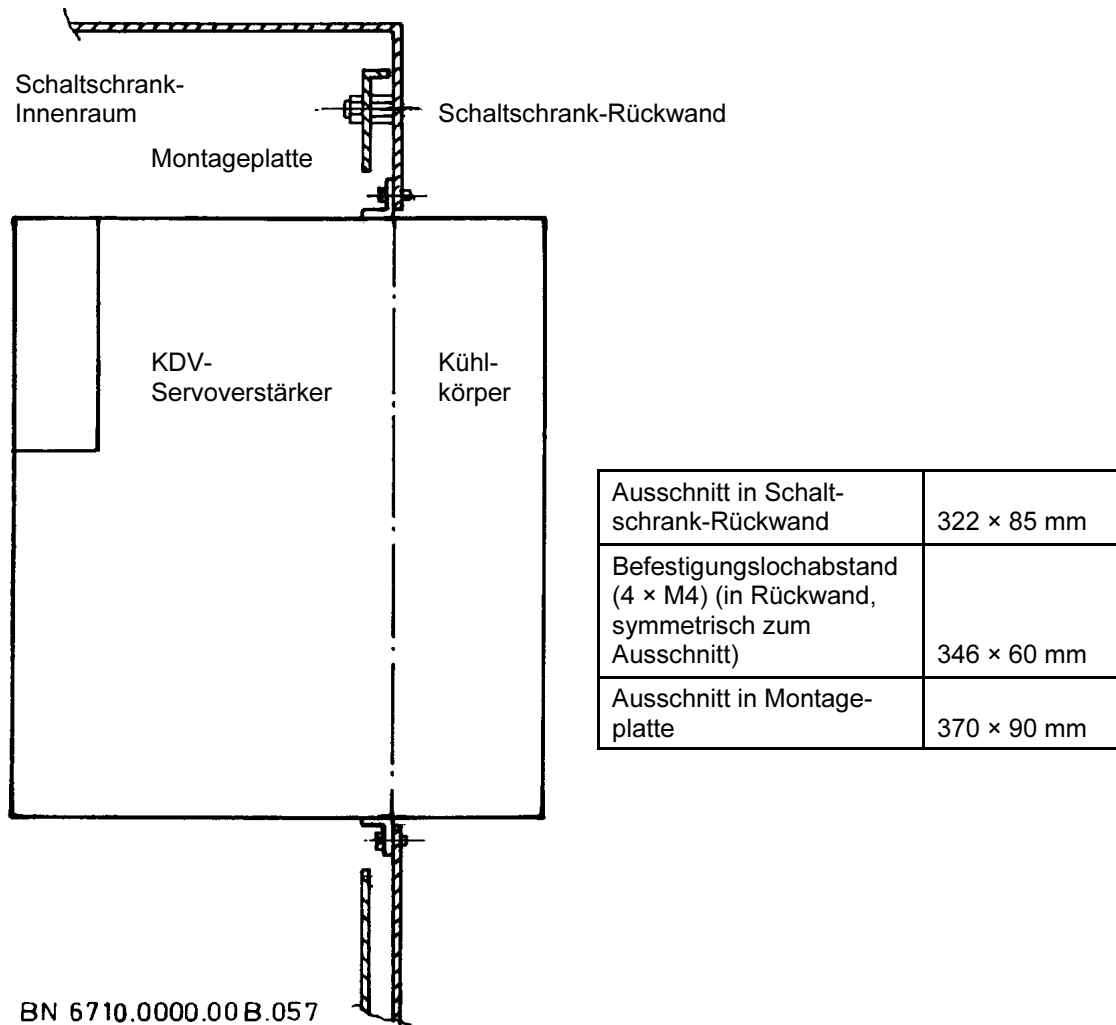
Montagesatz 086230, Seitenansicht Standardeinbau
